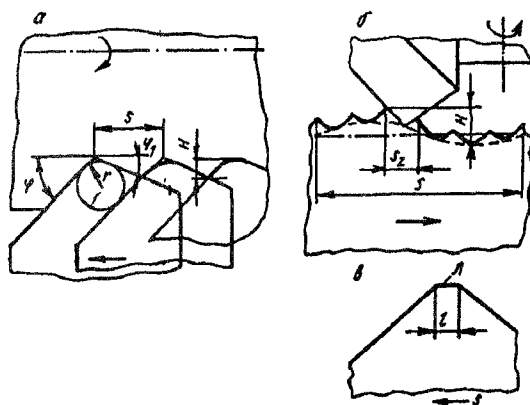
Формирование «геометрической» шероховатости при точении (а), торцовом фрезеровании (б) и резец с дополнительным режуще-зачищающим лезвием (в)
